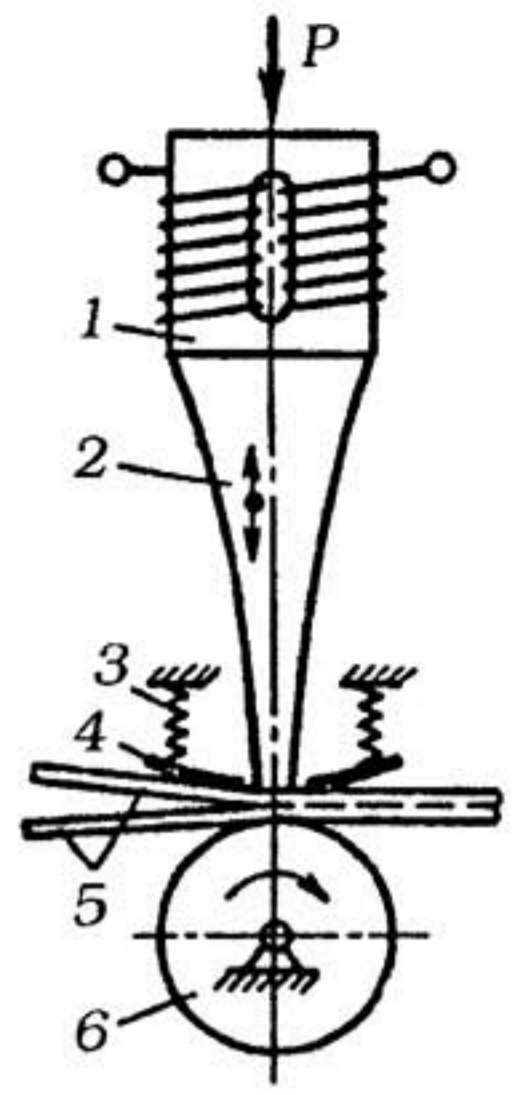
Схема роликовой ультразвуковой сварки: 1 — излучатель; 2 — концентратор; 3 — пружина; 4 — прижимный полз; 5 — свариваемые материалы; 6 — ролик
